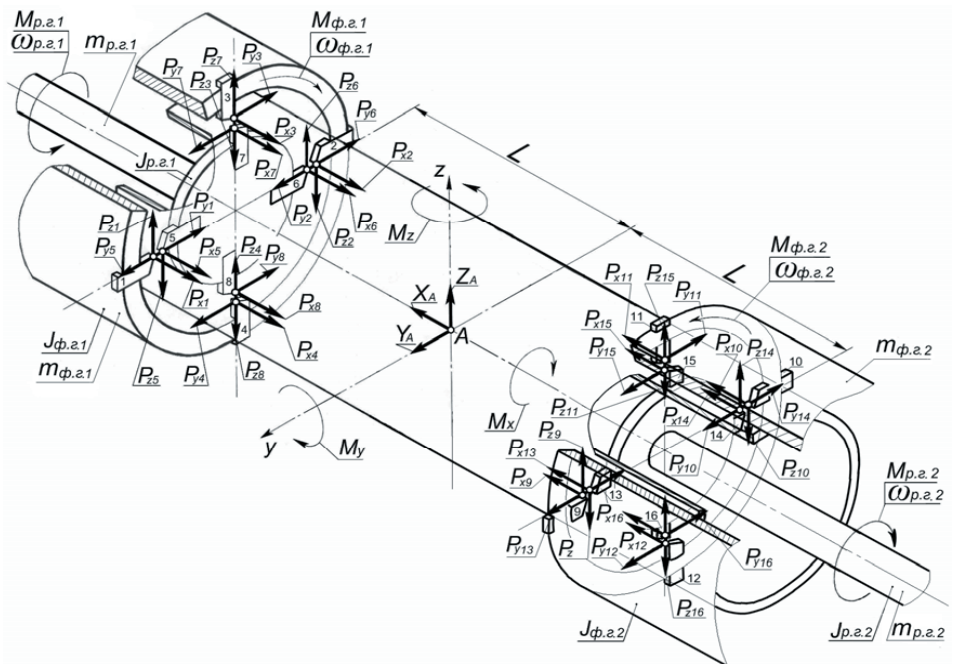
Розрахункова схема роботи пристрою для обробки кінців труб
